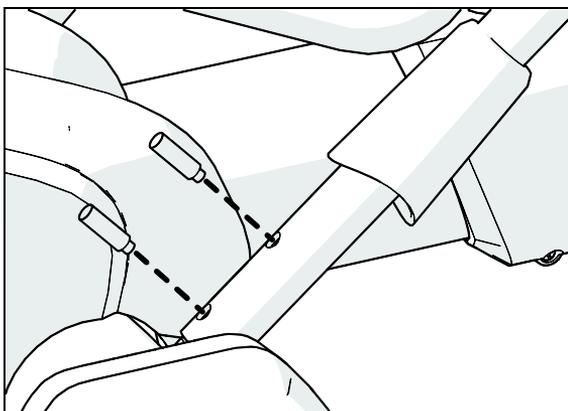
Remoção do parafuso do conjunto da barra de apoio
